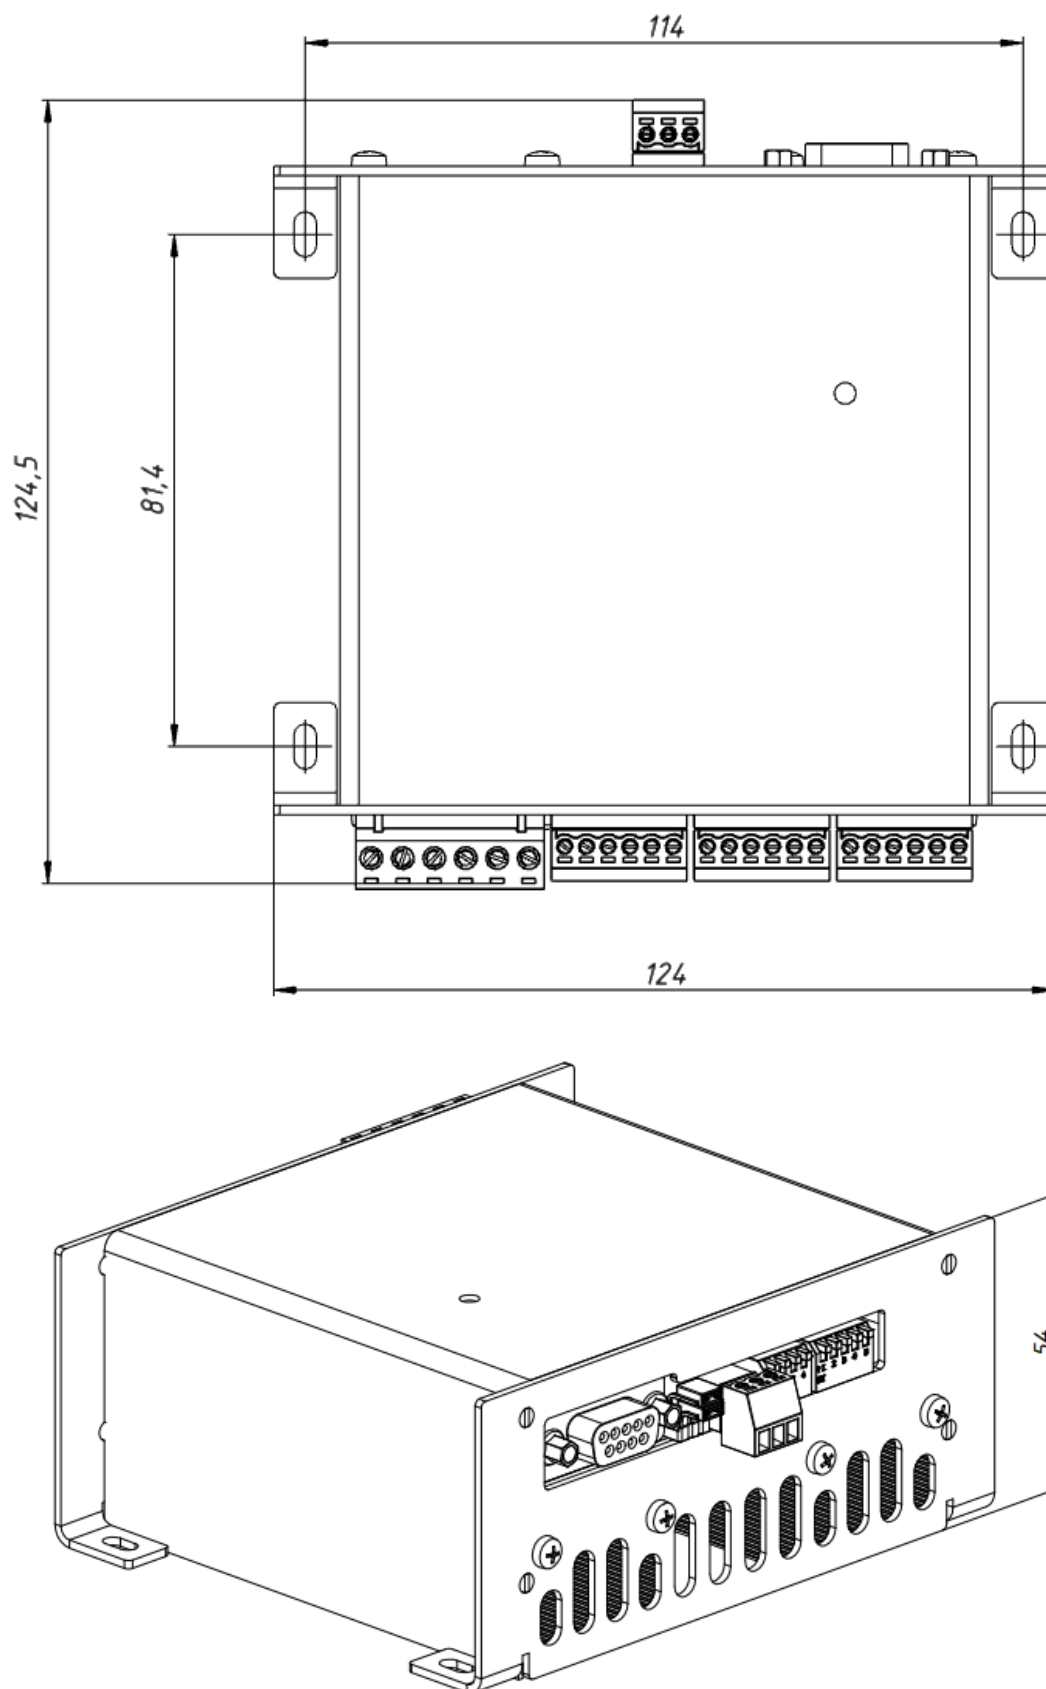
Габаритные и присоединительные размеры устройства
